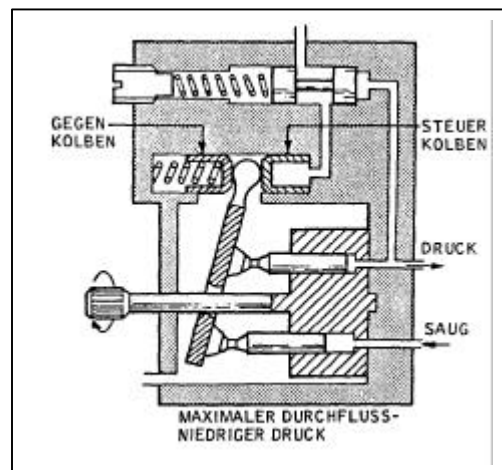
/ 7.2 Hydraulikpumpe Funktionsschema
